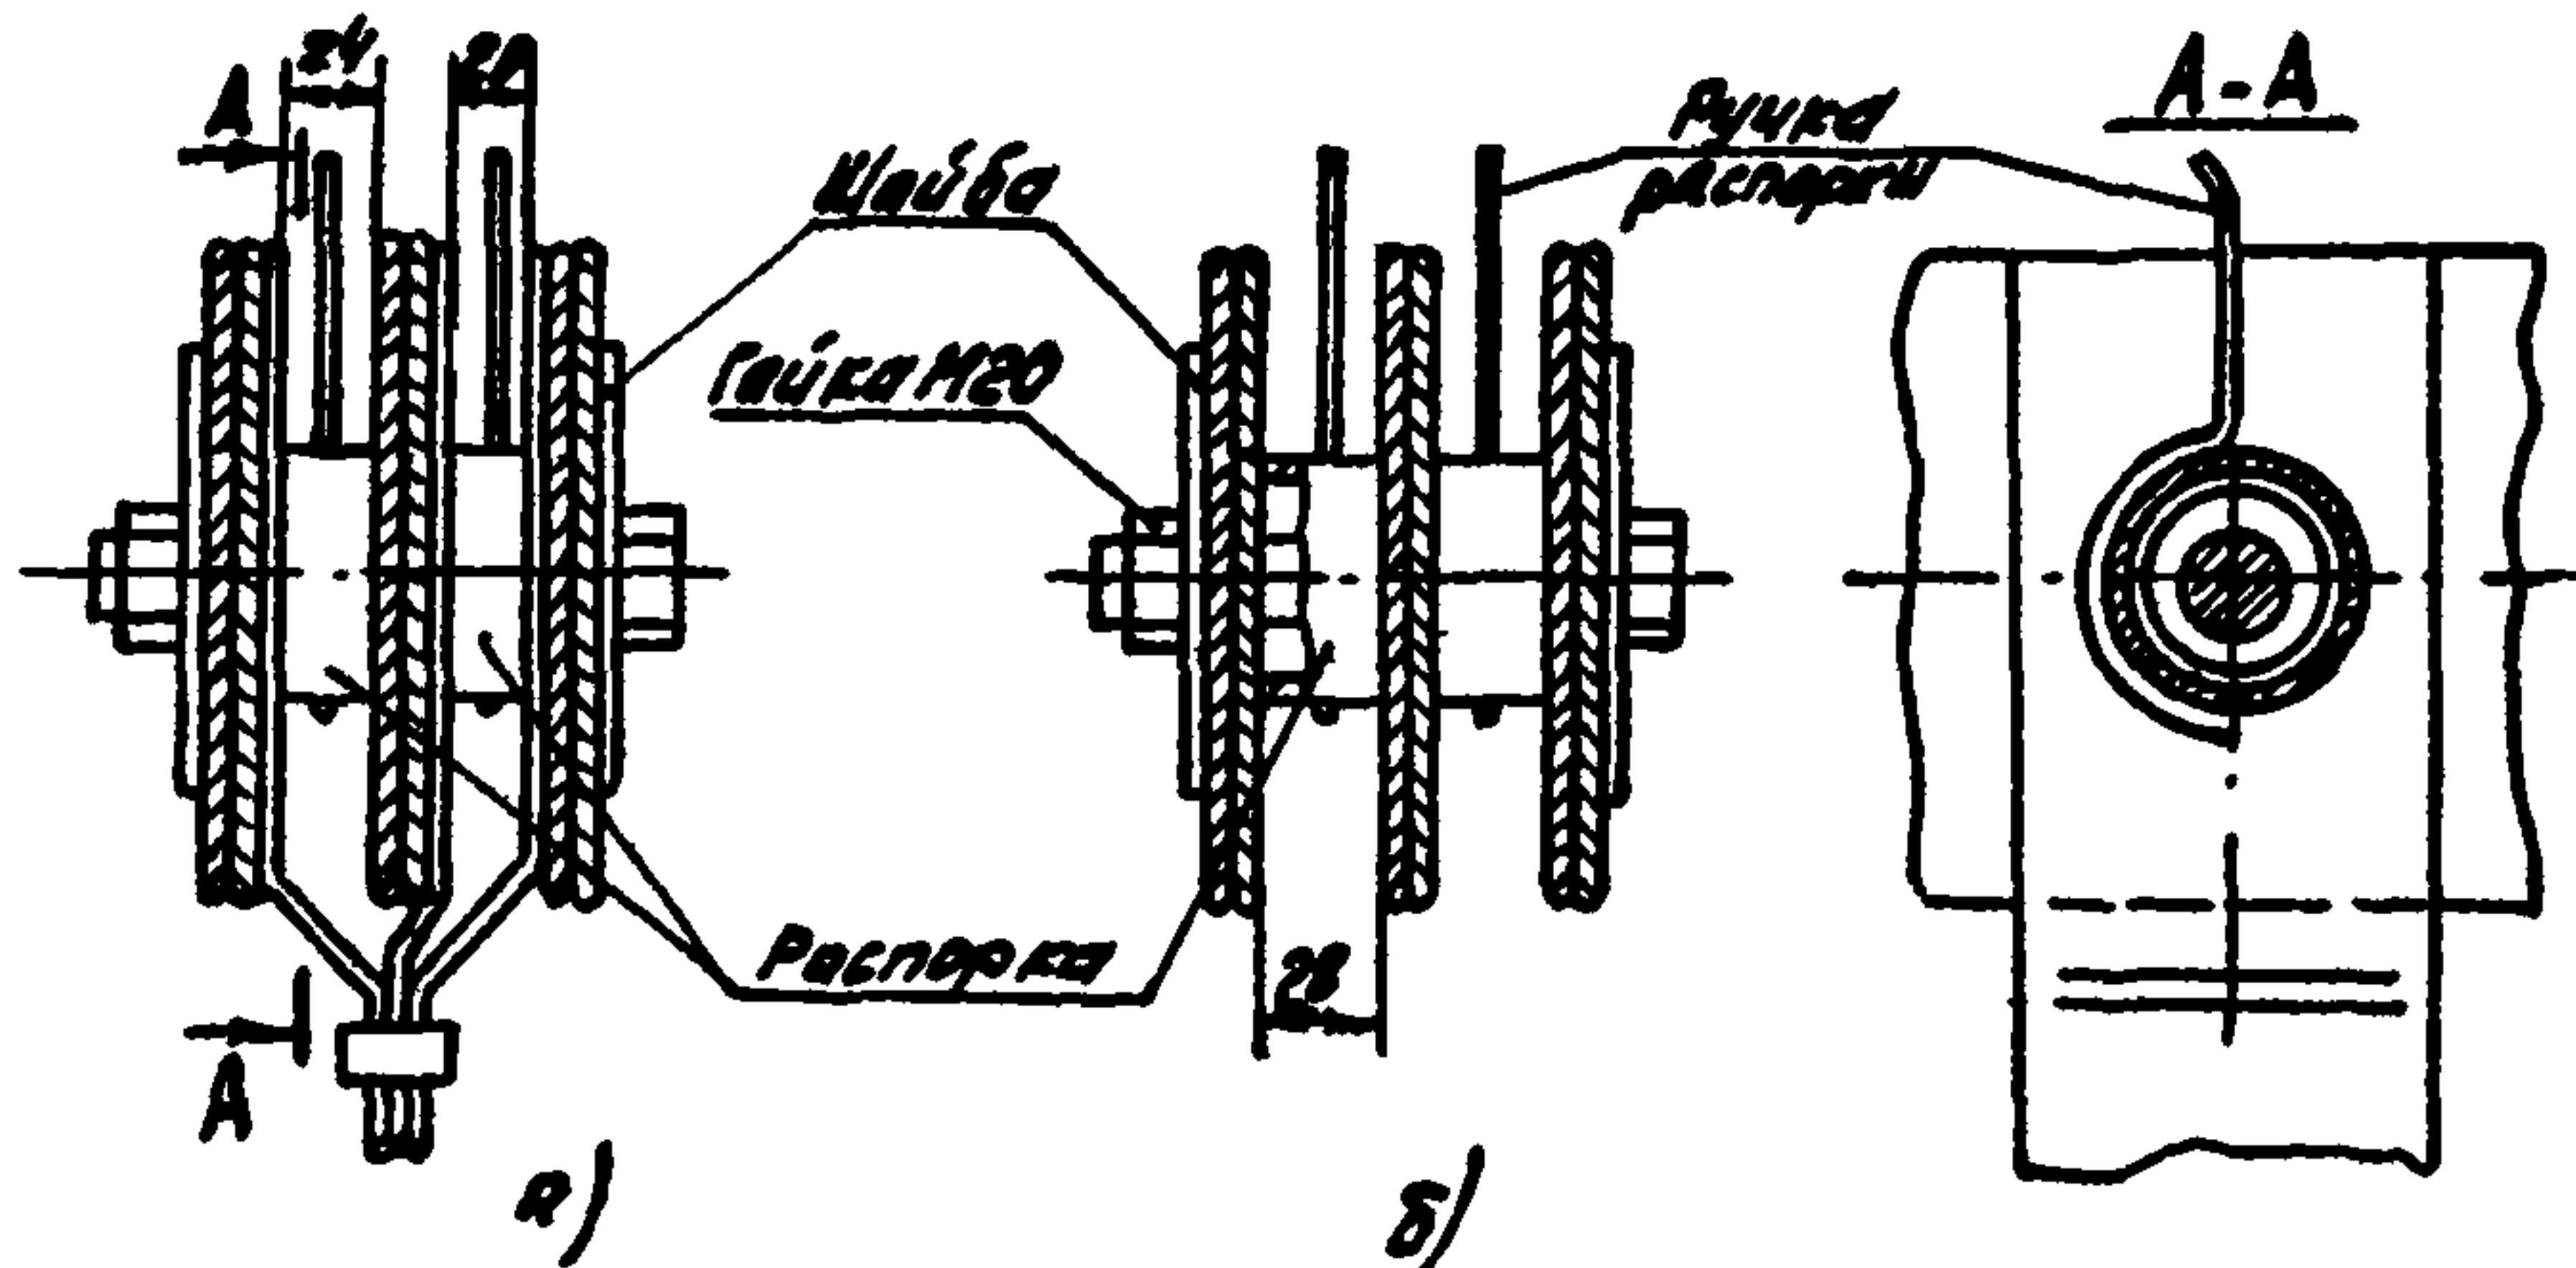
Кондуктор для сжатия шин перед сваркой секций шинопровода:
